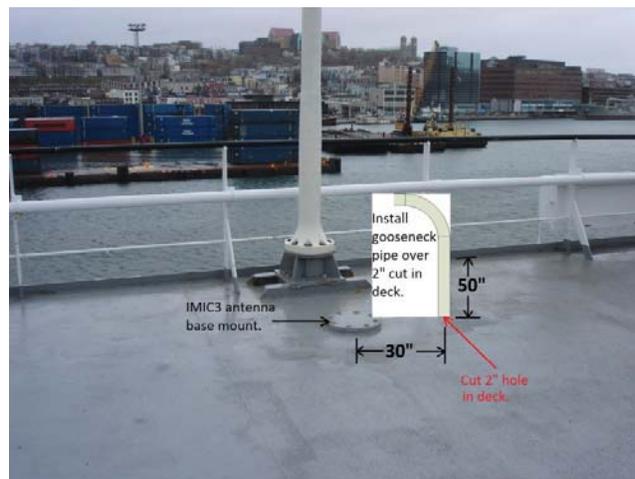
Emplacement du trou de 2 po et de la soudure pour le tuyau en col de cygne
